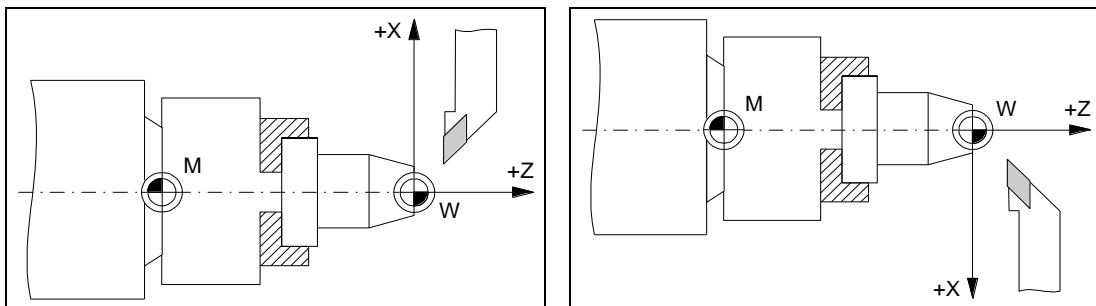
Розташування нульової точки заготовки при роботі на токарному верстаті з ЧПК
